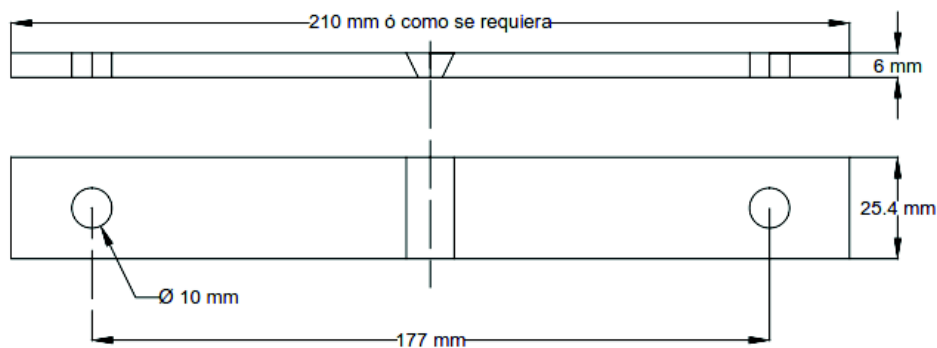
Dimensiones de probeta para ensayo de corrosión.
